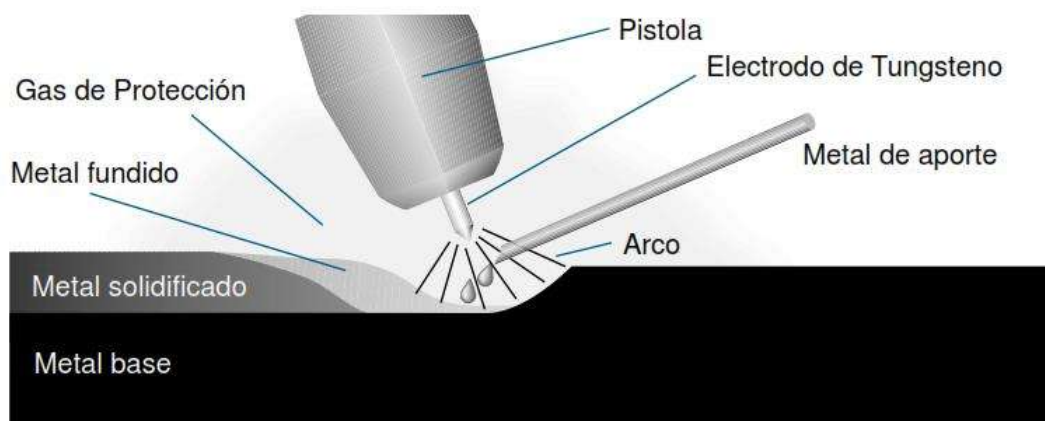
Ilustración esquemática de una soldadura por sistema TIG [29].
